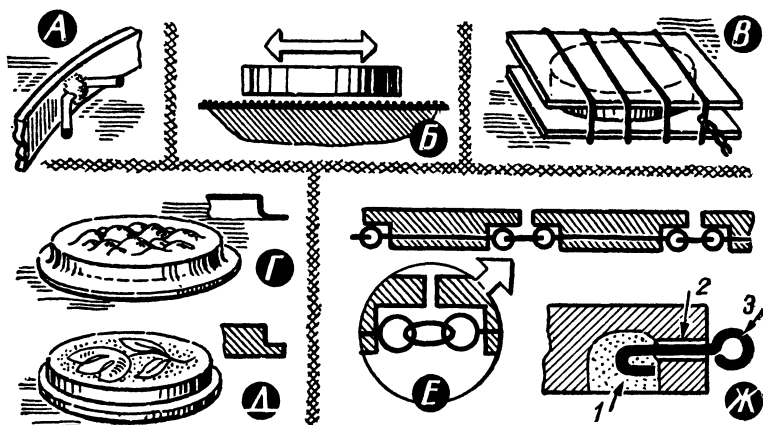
Литье с обрамлением: А — укрепление приливов в обрамлении; Б — шлифовка обрамления; В — упаковка перед полимеризацией; Г — вставка из басмы; Д — гравированная вставка; Е — вариант крепления элементов браслета: 1 — выемка; 2 — отверстие; 3 — проволочная петля; Ж — установка арматуры после отливки.
